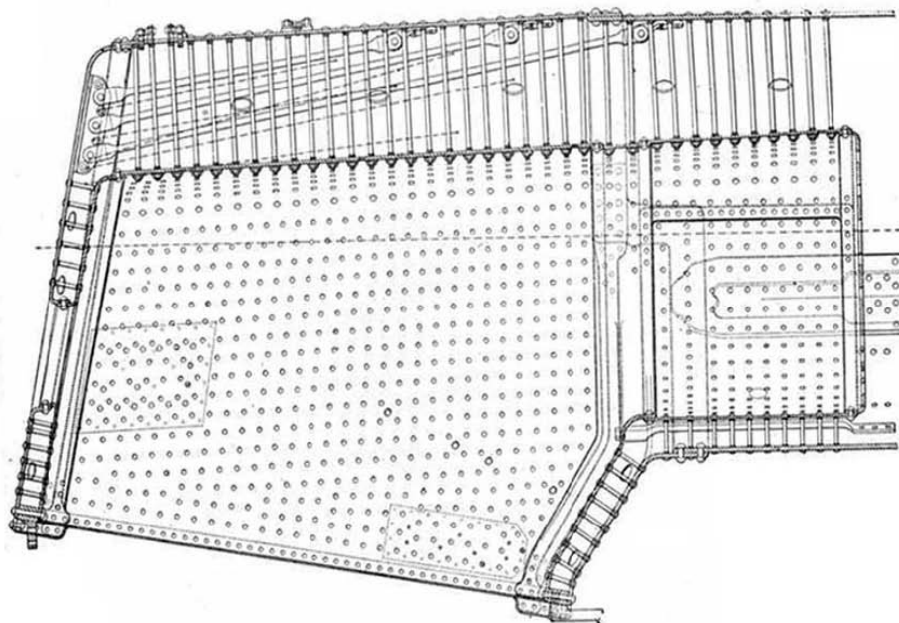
Hogar de cobre de las locomotoras Mountain del P.L.M. Corte longitudinal
